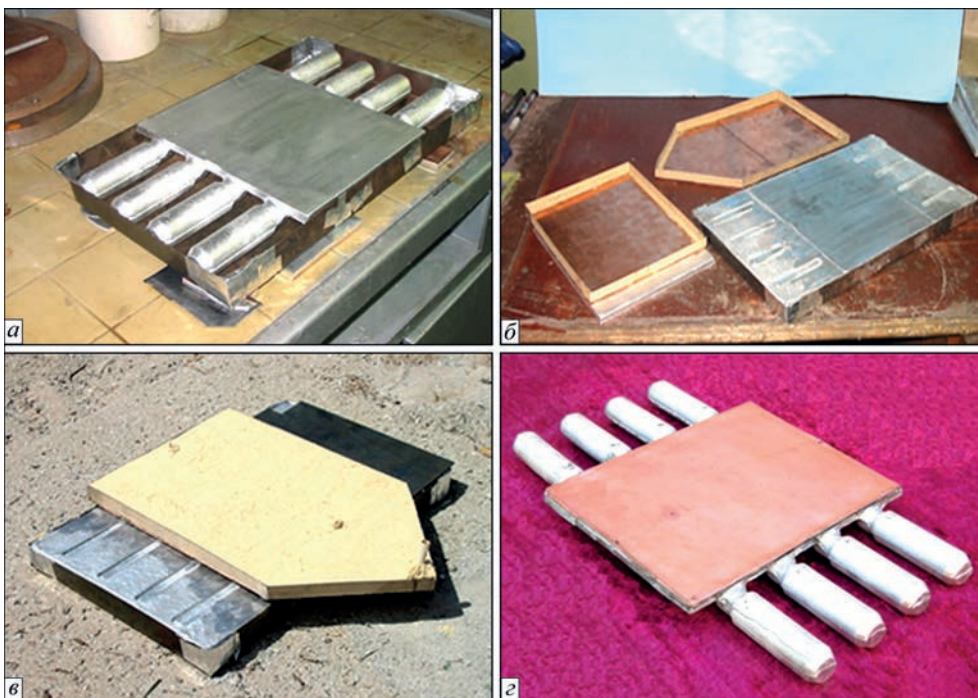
Загальний вигляд до (а) і після (б) заливки сплавом Вуда, який повністю заповнив простір між матрицею і алюмінієвою заготовкою і тим самим утворив монолітну заготовку для зварювання вибухом; в – установка мідної пластини з вибуховою речовиною для подальшого плакування вибухом; г – заготовка з декількох обтискних клем перед розрізанням
